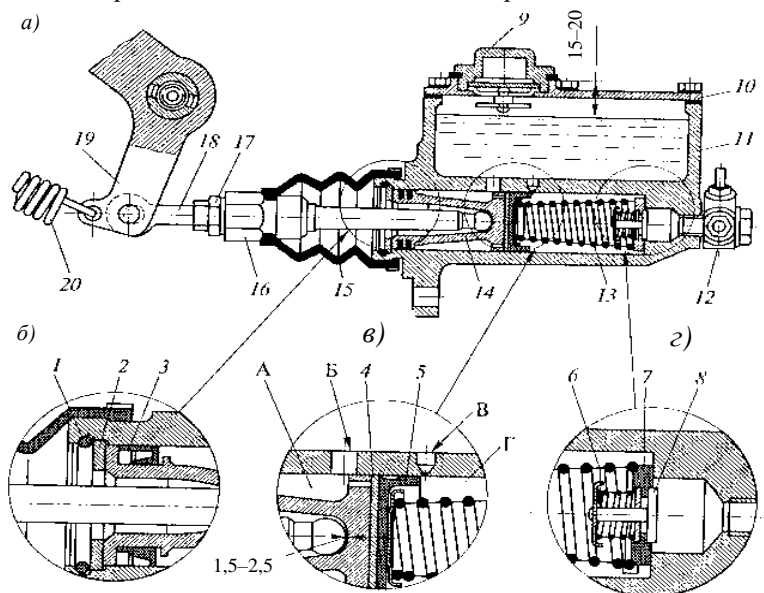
Главный тормозной цилиндр одноконтурного гидропривода: а – устройство; б – уплотнение задней части поршня; в – поршень; z – клапан; 1 – стопорное
